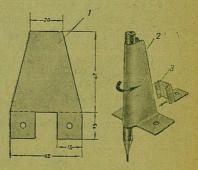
Стойка пишущего устройства: 1—развертка жести для стойки, 2—изгибание стойки на карандаше, 3—скрепляющая скобка.
